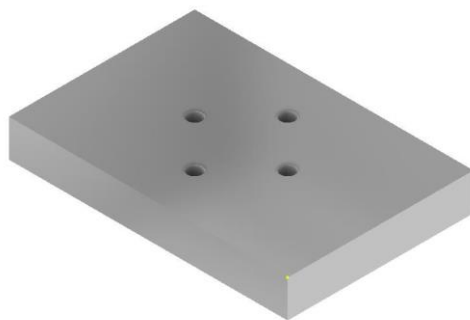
Τρισδιάστατη απεικόνιση αποστολής 18
